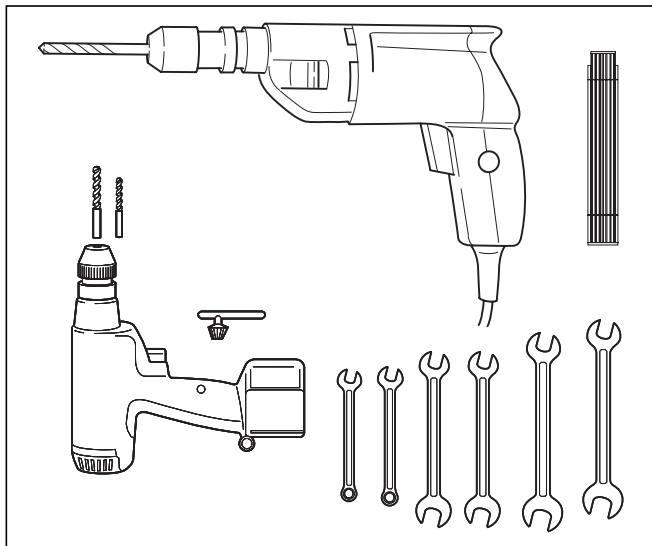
Benötigtes Werkzeug bei Montage an Fassaden
